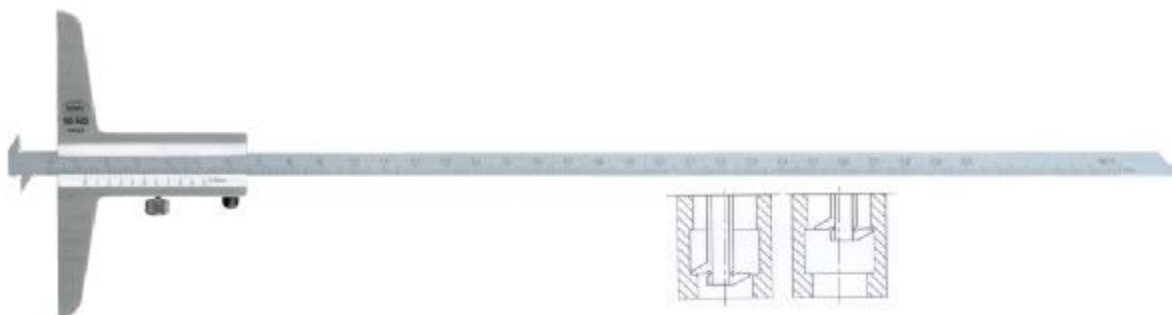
Общий вид и принцип действия штангенглубиномера нониусного MarCal 30 ND
